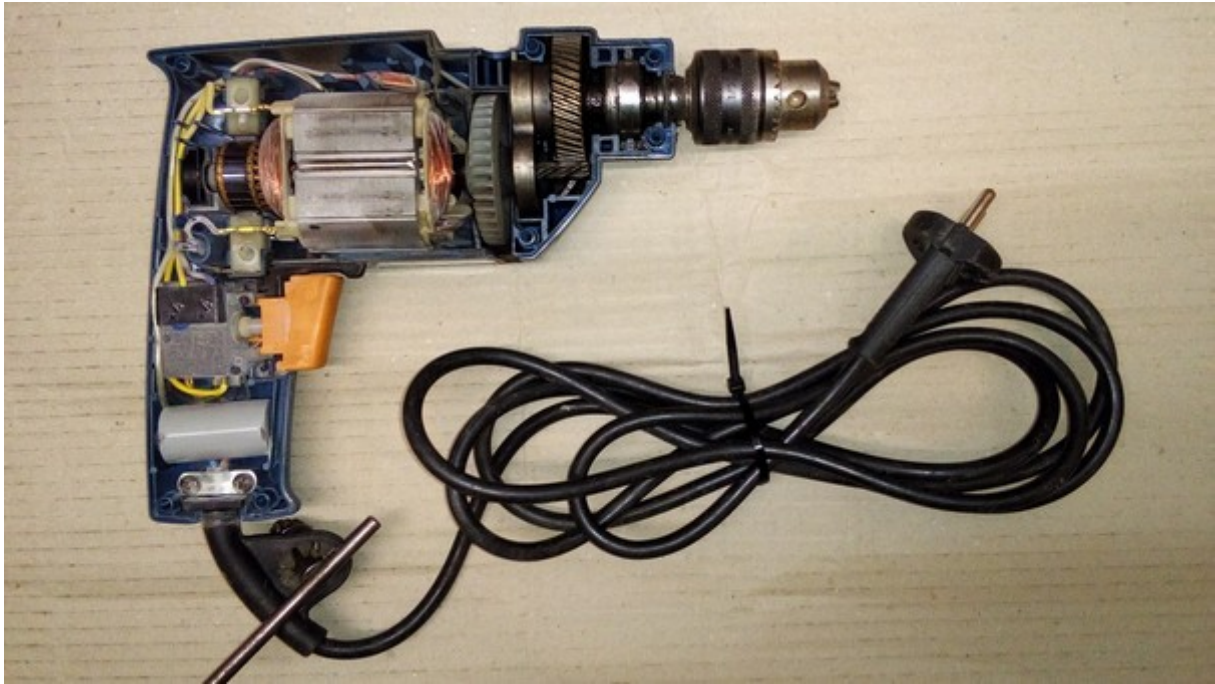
Getriebe, Elektromotor und andere Komponenten innerhalb der Bohrmaschine
